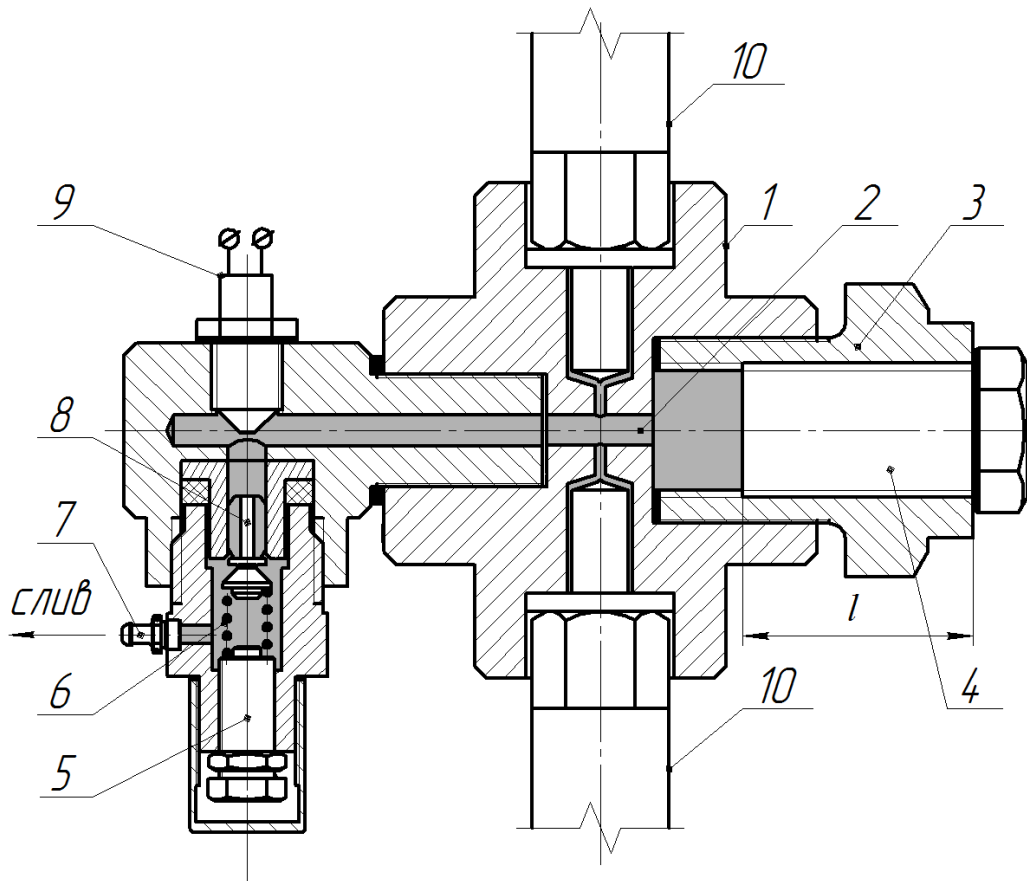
Экспериментальное УПВ с гидравлическим аккумулятором (объем его выделен затемнением): 1 и 2- корпус и камера впрыска; 3- штуцер; 4- сменный шток; 5- регулировочный винт затяга пружины; 6- пружина перепускного клапана; 7- сливной штуцер; 8- перепускной клапан; 9- датчик давления серии МД; 10- форсунки;  $l$ - длина штока
